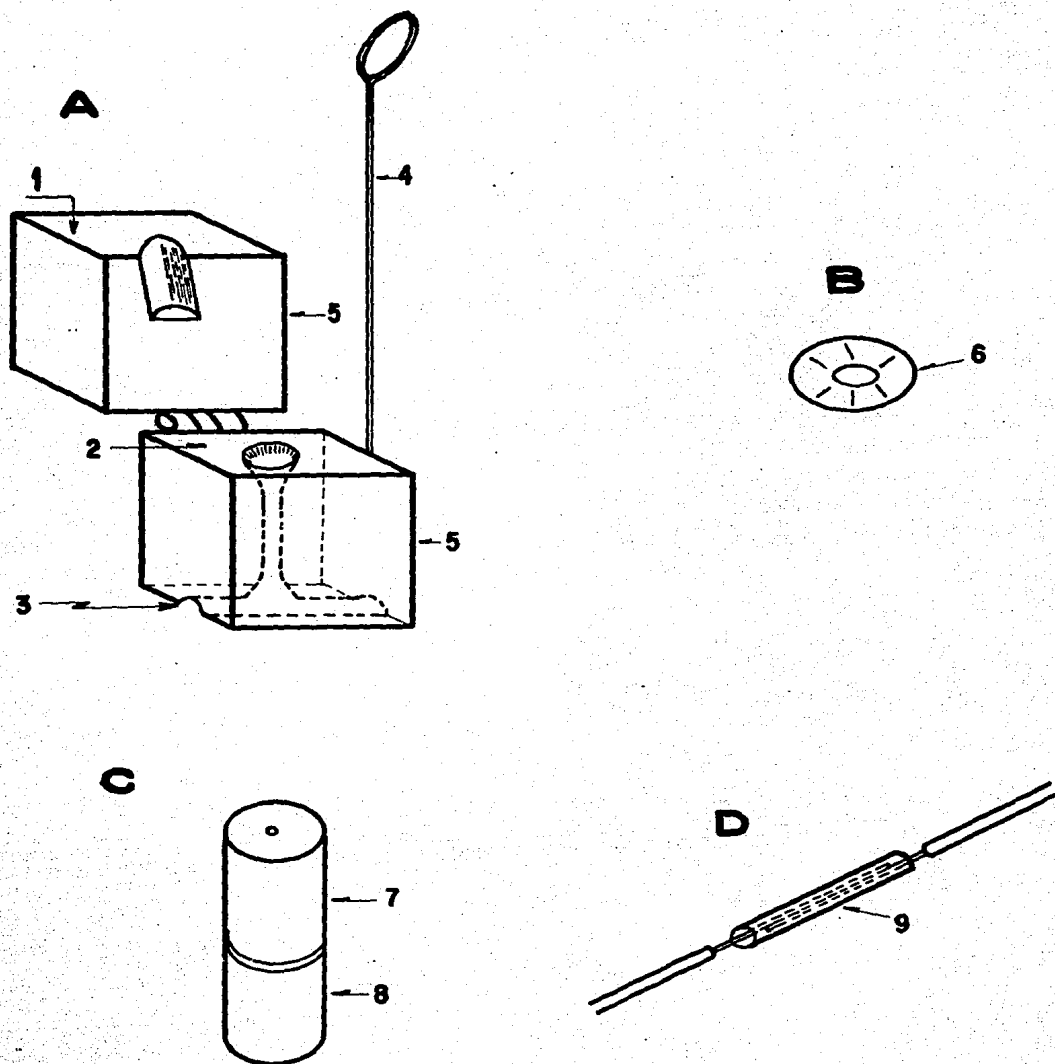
SOLDADURA TIPO TERMITA.
